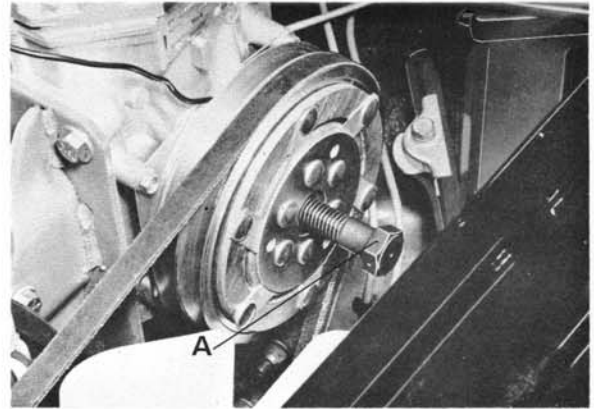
Ausbau der Kompressor-Riemenscheibe
